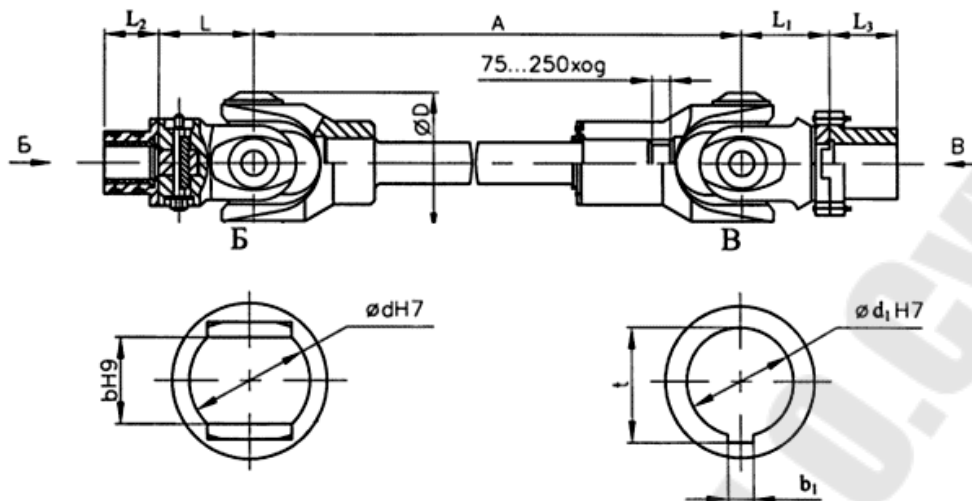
Шпиндель карданного типа на подшипниках качения.
